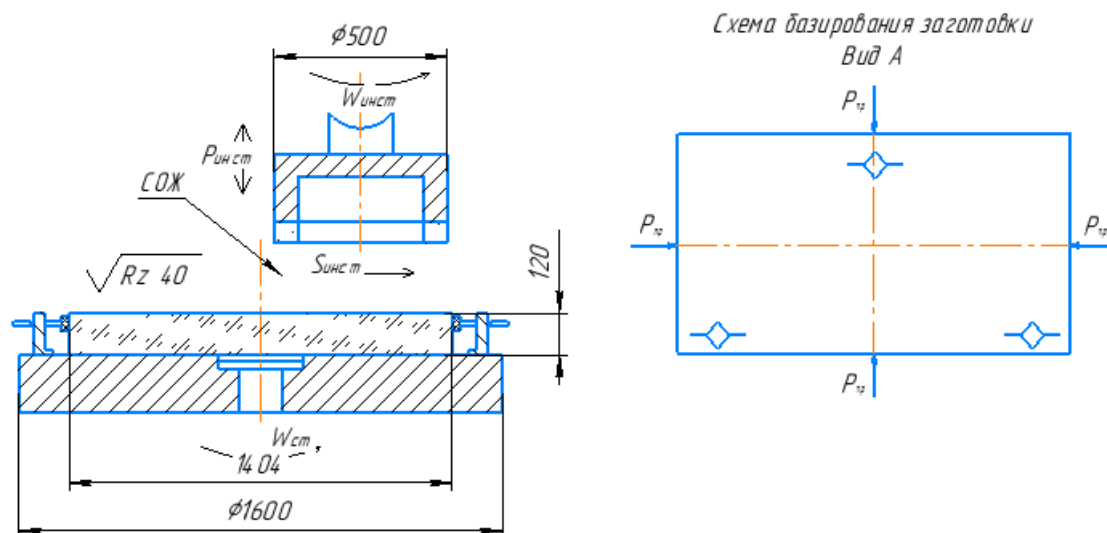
Эскиз операции фрезерование на станке ВС3-45
